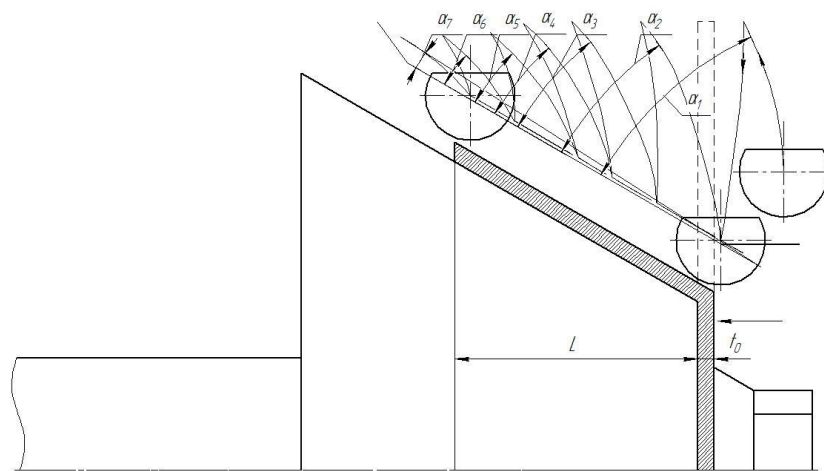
Послідовність ротаційної витяжки заготовки та траєкторії руху інструмента
